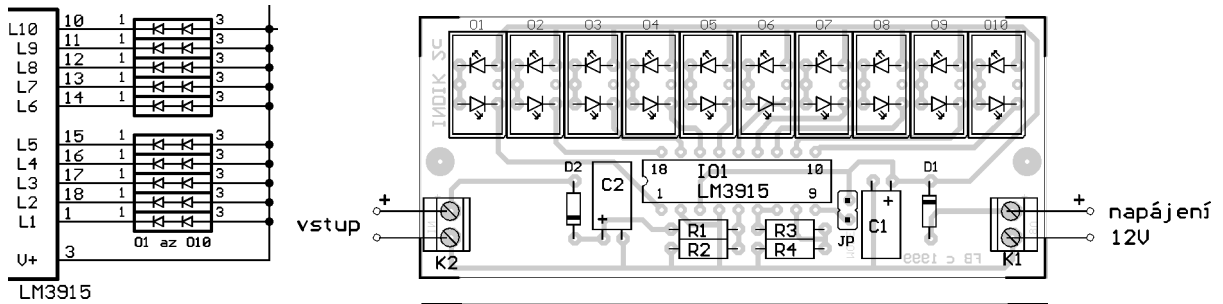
Deska s plošnými spoji pro indikátor 2a
